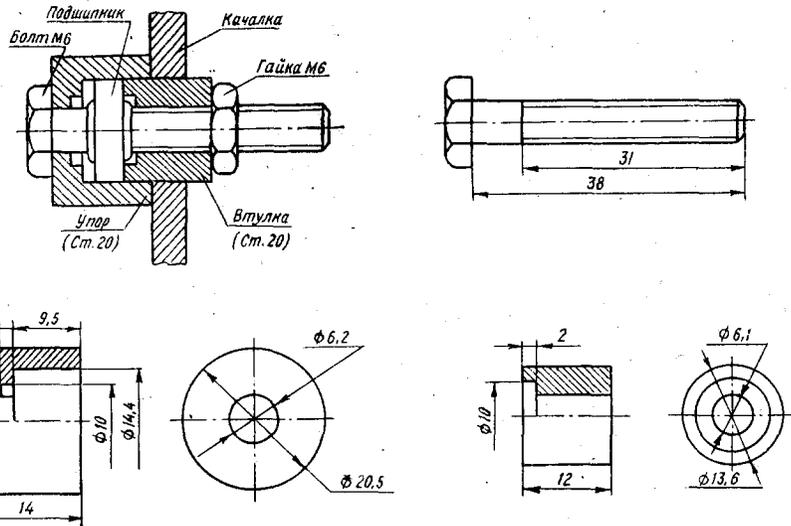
Приспособление для выпрессовки подшипников Ш6, ШС-6 и резиновых вкладышей из качалок и поводков в системе управления двигателем
